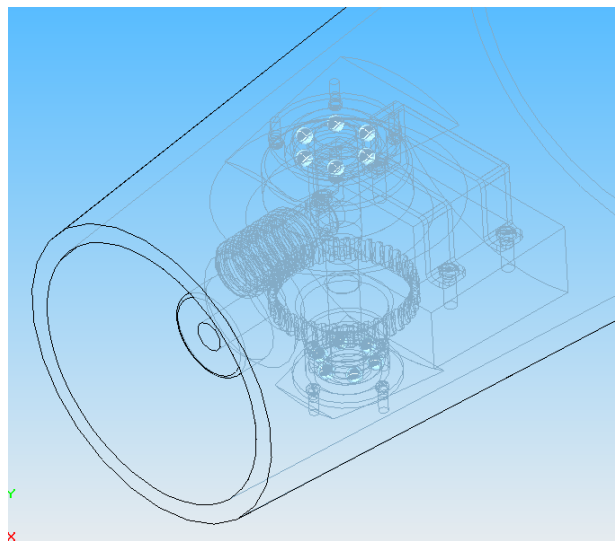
Ensamble del engranaje para movimiento en la muñeca
